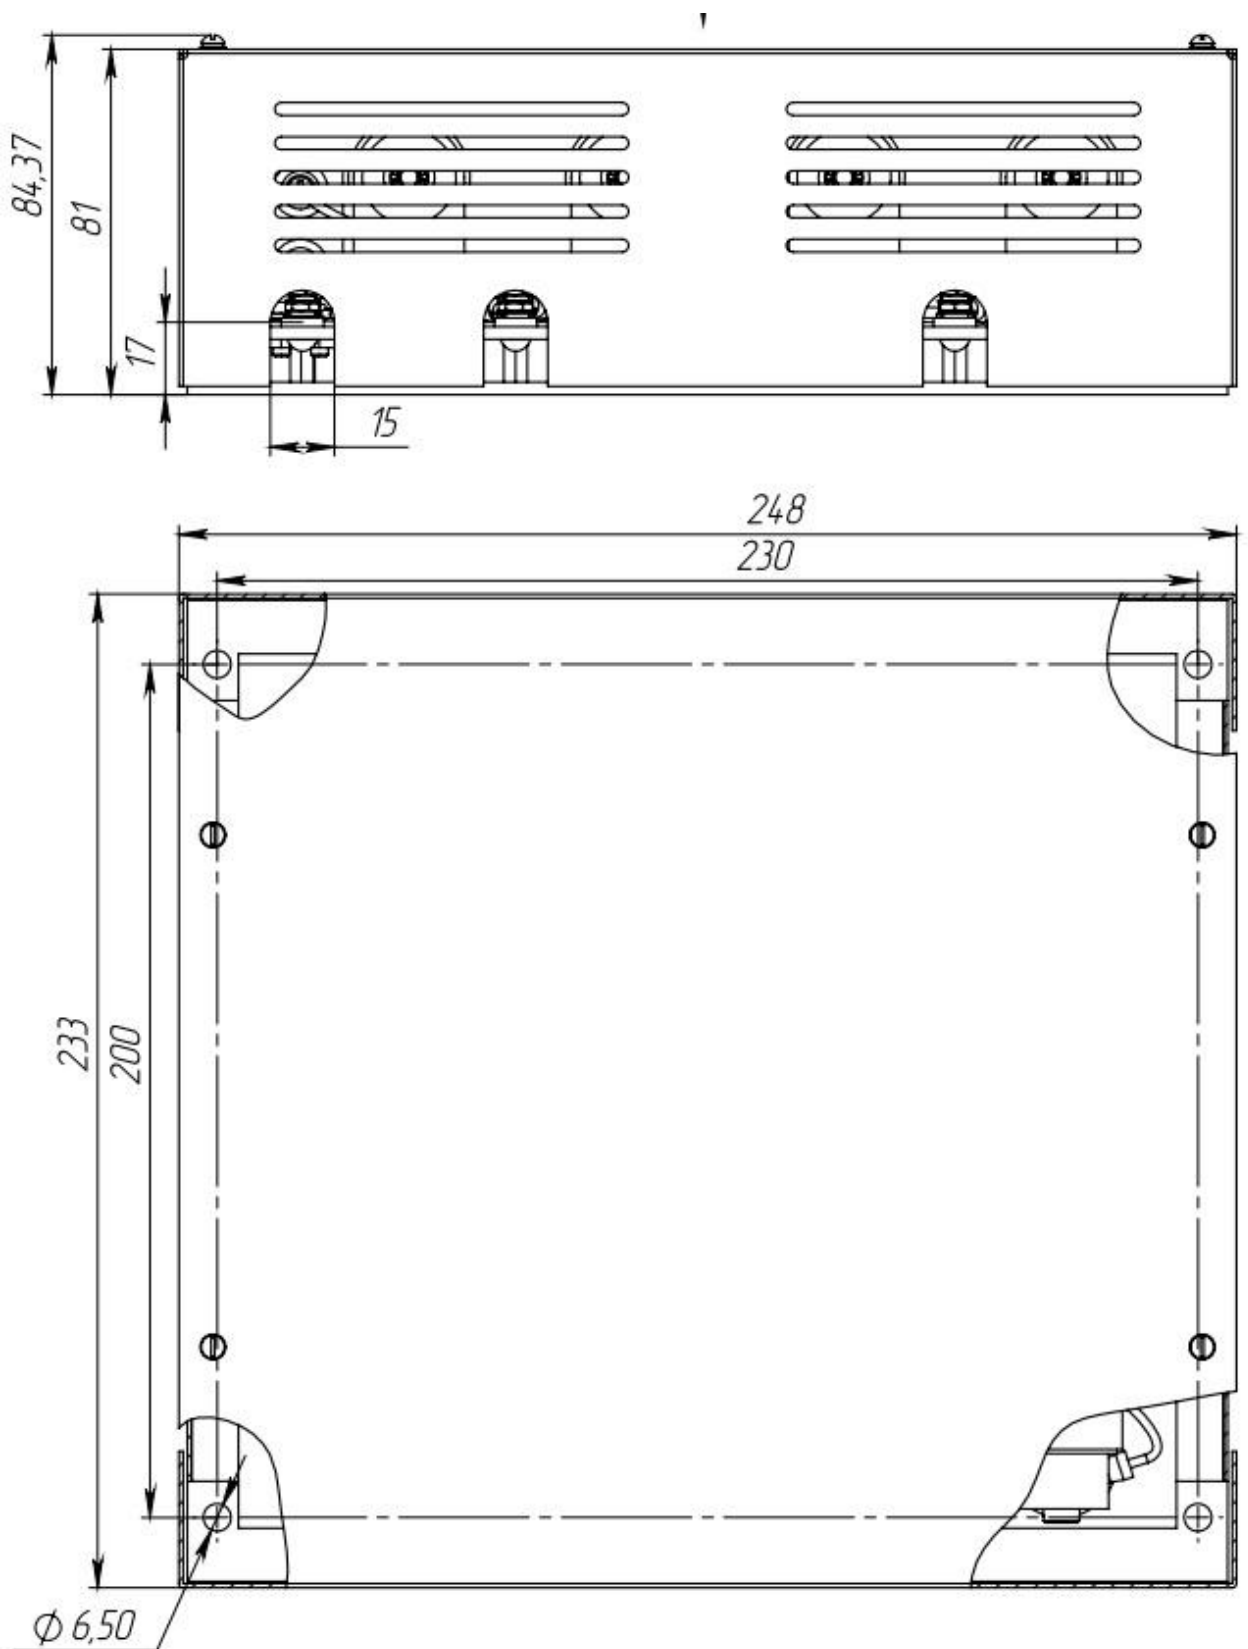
Габаритные и установочные размеры БЩП
